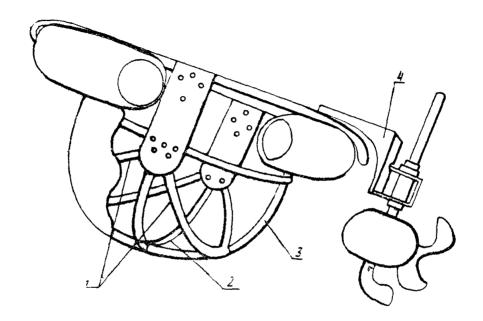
Складное портативное плавсредство: I — промежуточные полуобручи; 2 — ц ітрельный полуобруч; 3 — полые трубки; 4 — насядка для крепления моторе
